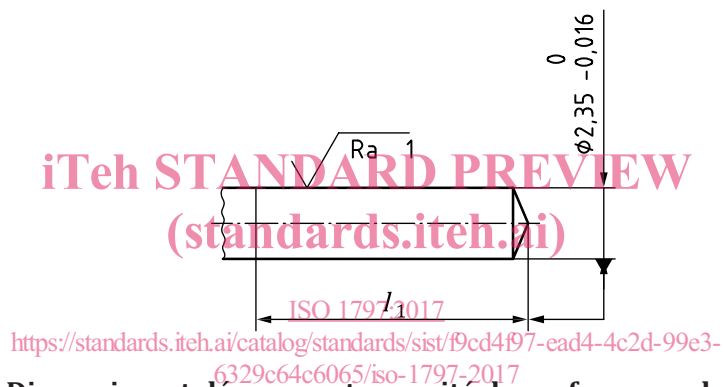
Dimensions, tolérances et rugosité de surface pour les queues du type 2
